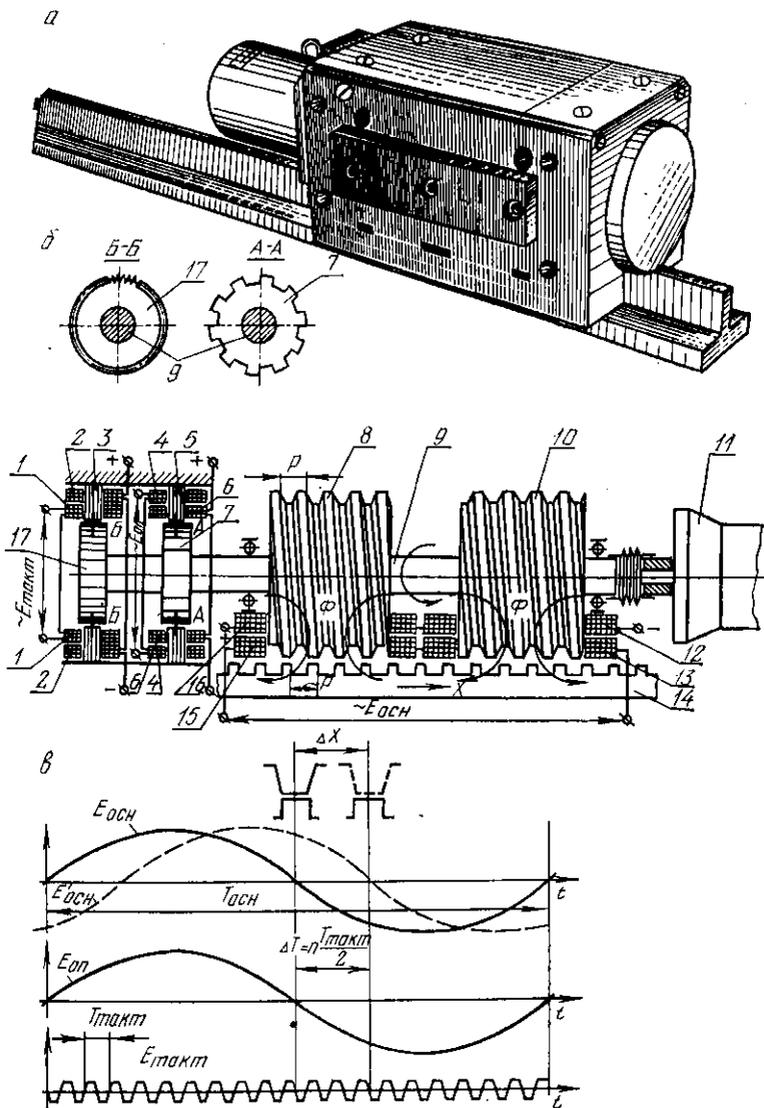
Линейный измерительный преобразователь типа ДЛМ-11:
